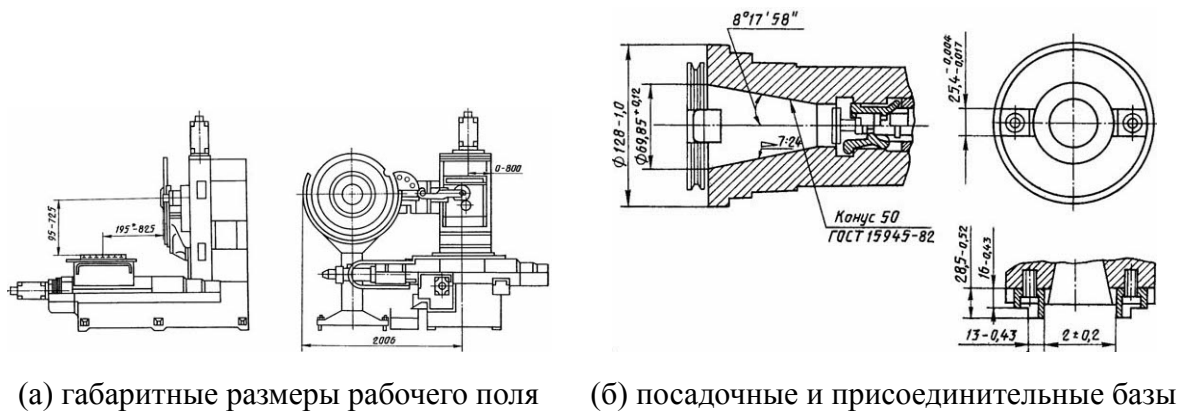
Посадочные и присоединительные размеры станка 2206ВМФ4
